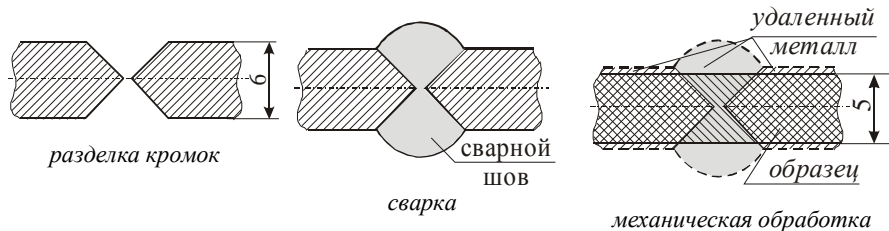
Этапы изготовления сварного образца для исследования жесткости
